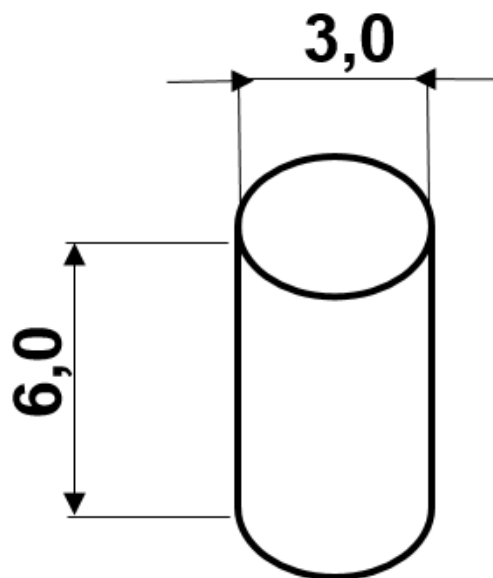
10-Desenho do corpo de prova para o ensaio de compressão (dimensão em mm).
